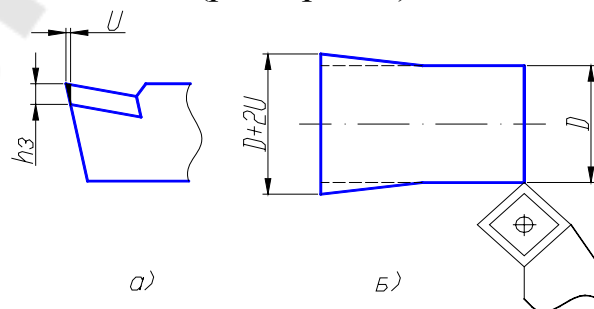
Изменение размеров обрабатываемой детали при наличии радиального износа резца
